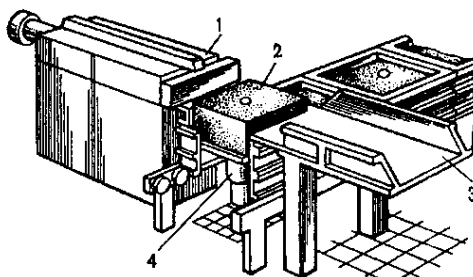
Автоматическая установка для выбивки отливок из форм:
